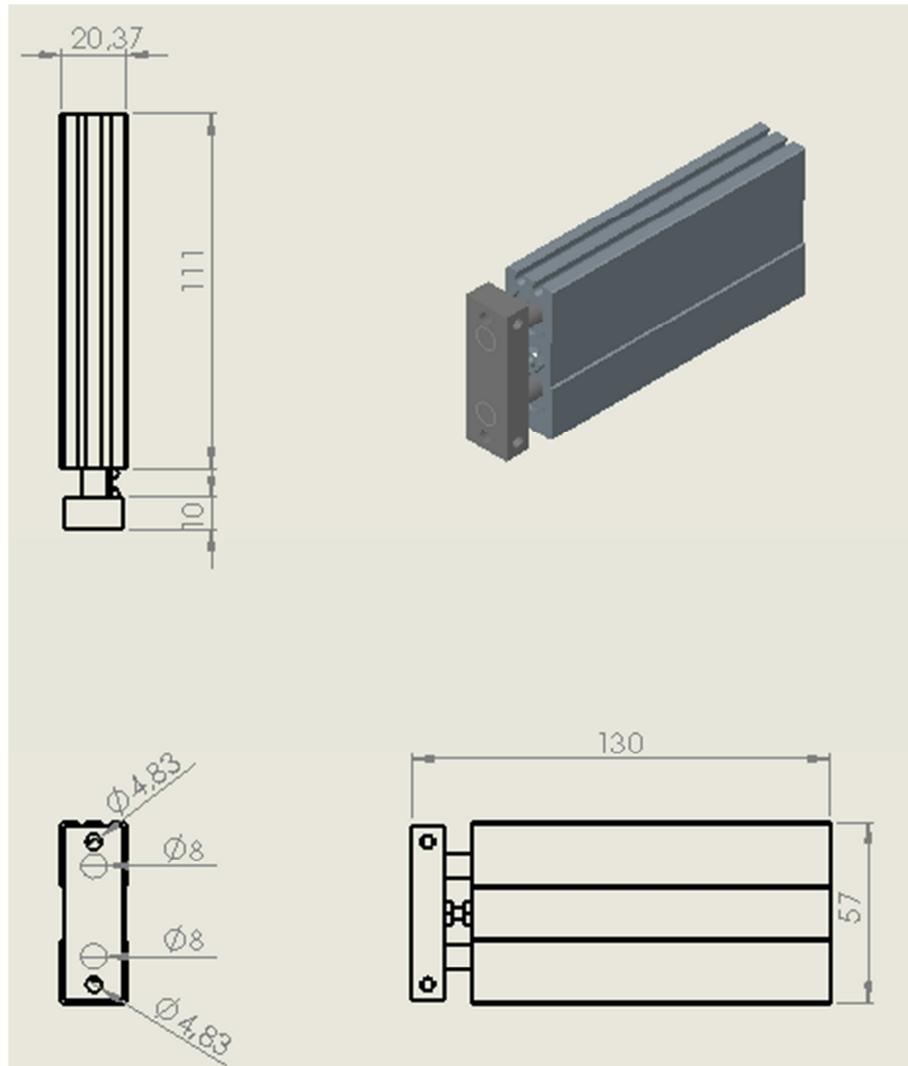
Cilindro Multimontaje del Pick and Place.
